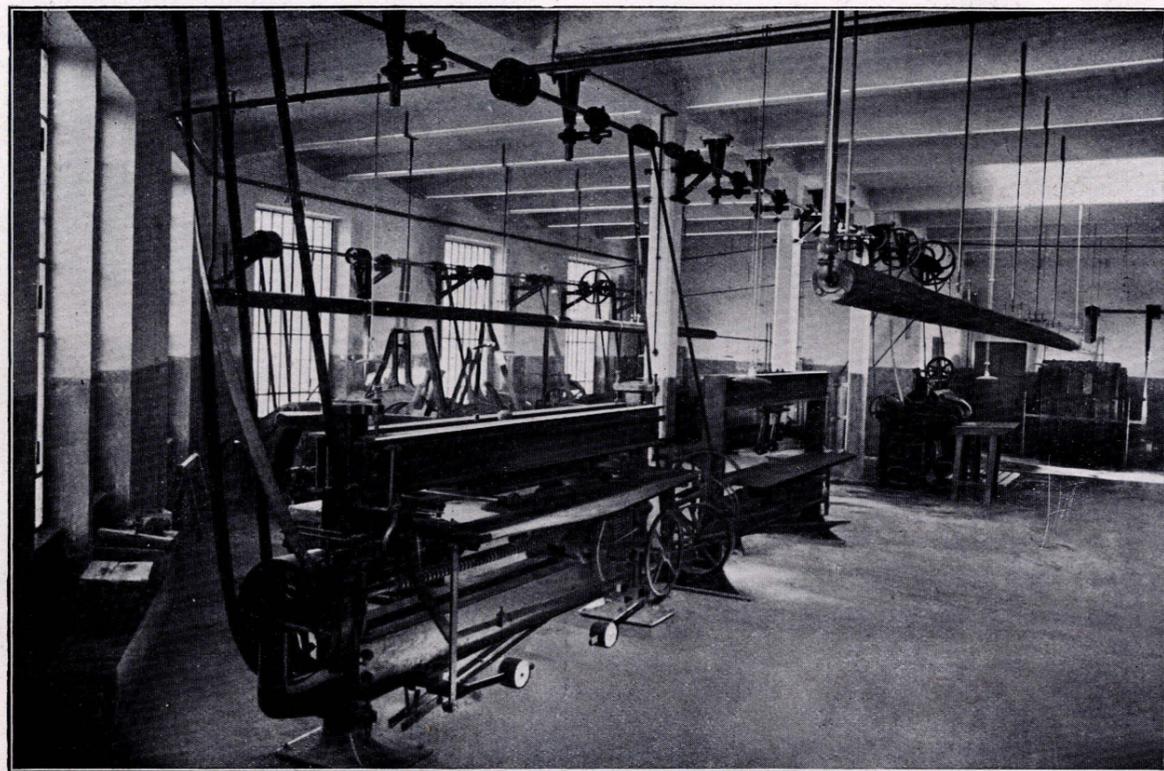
Laboratorio tecnico di conceria — Sezione rifinizione a macchina.
